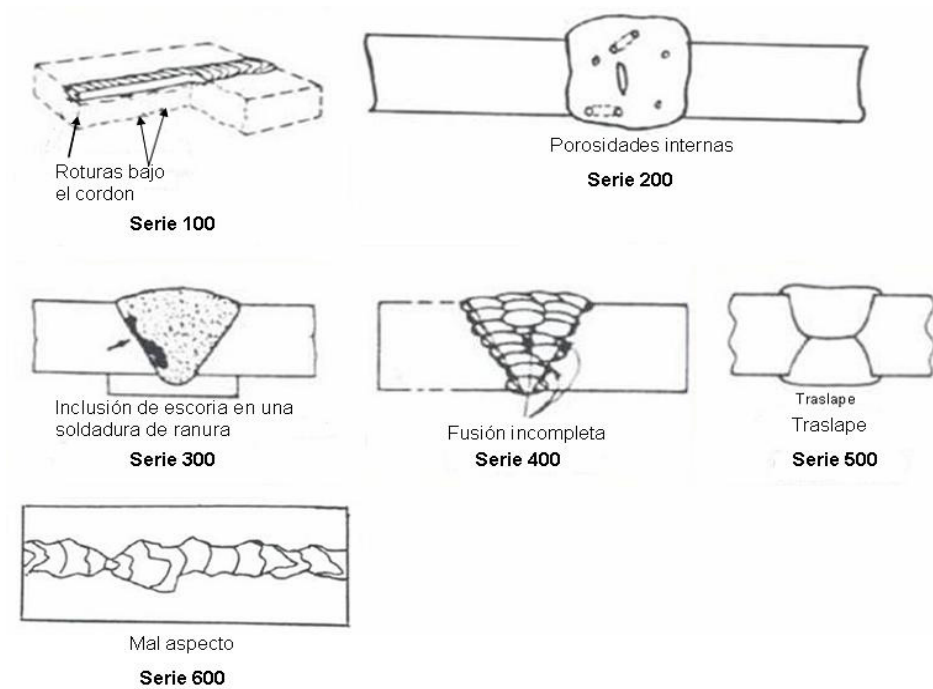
Clasificación de los defectos en las soldaduras según IIW [13].
